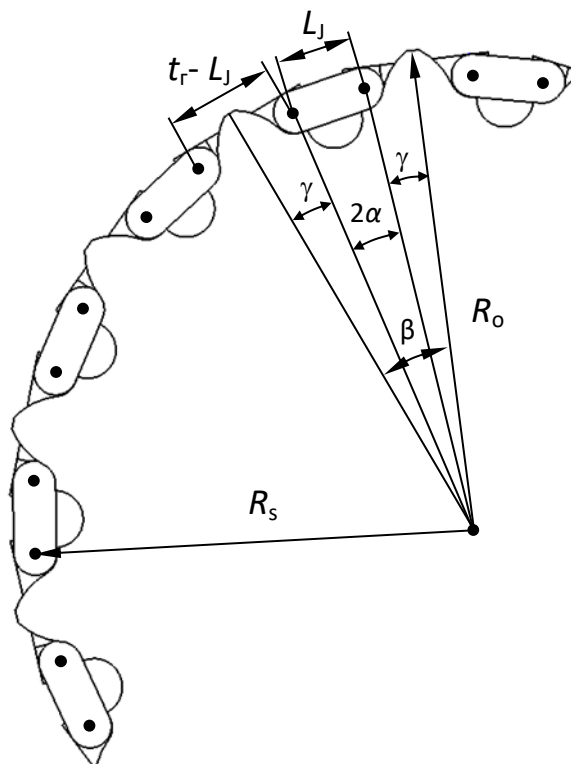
Параметры звездочки для гусеницы с параллельными шарнирами
